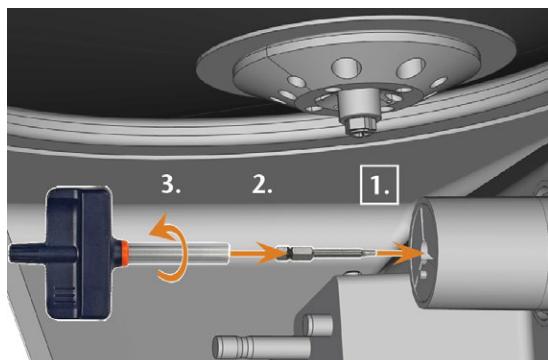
DESSERRER LA VIS DE LA PINCE DE SERRAGE DU SUPPORT DE PIÈCES BRUTES
